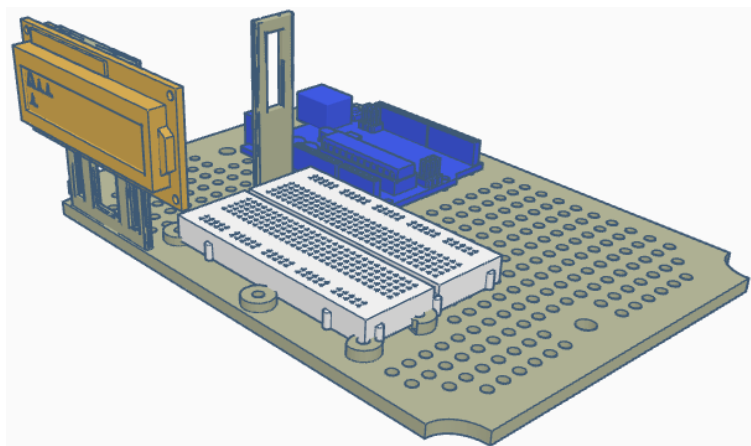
3D-модель корпусу автоматизованої системи з компонентами [36]
